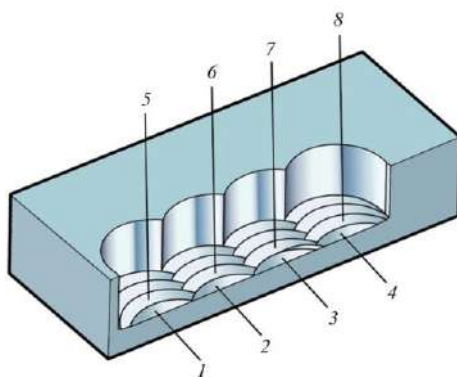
Оброблення вибірки від дна з поступовим підняттям різального інструменту при плунжерному фрезеруванні [5]
